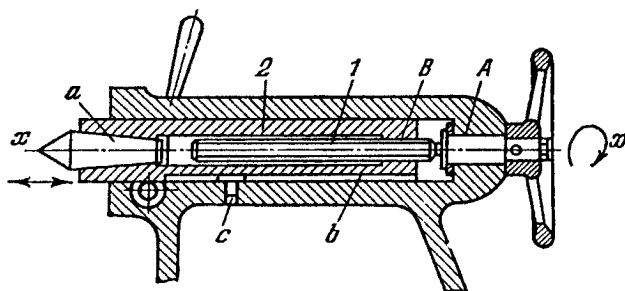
Гвинтовой механизм задней бабки токарного верстака:
